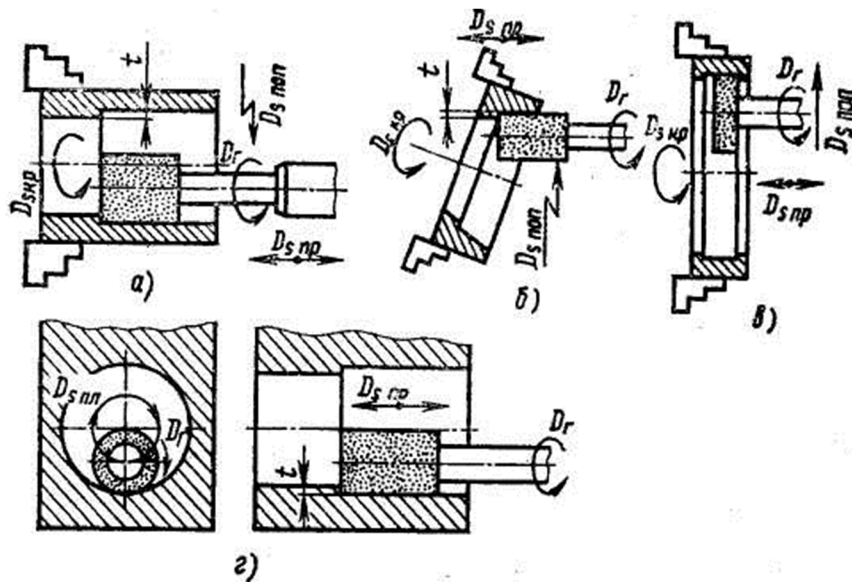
Схемы обработки заготовок на внутришлифовальных станках
